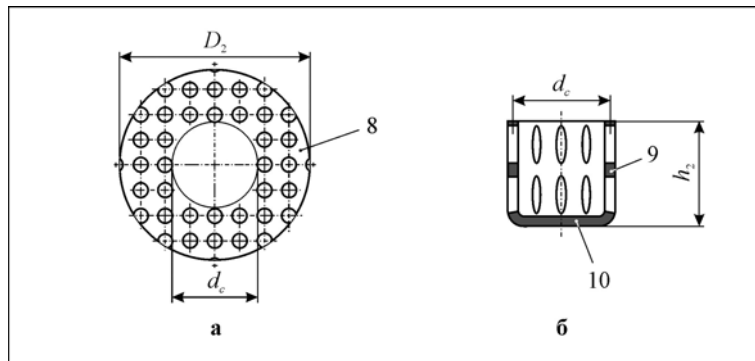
Заготовка (а) та деталь (б) після витягування за пунктом 2
